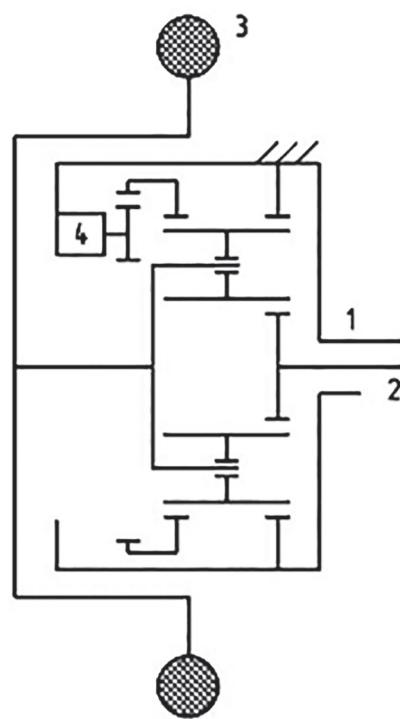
Модифицированный колесный редуктор (подшипники опор не показаны):
